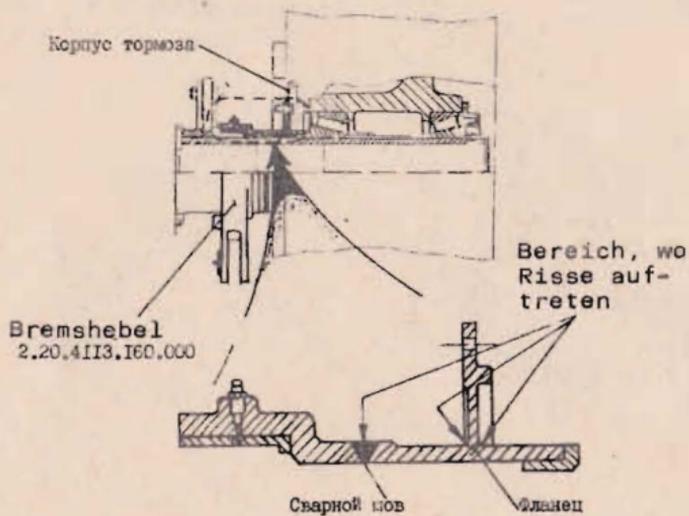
Hauptfahrwerkstraverse (zu Pkt. 5.5.1.8.)
